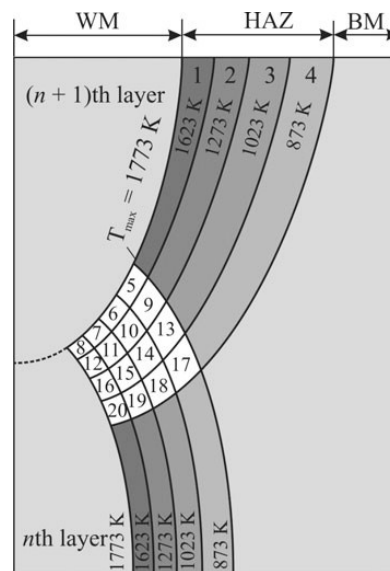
Zonas afectadas por el calor en la soldadura multipases [44].
